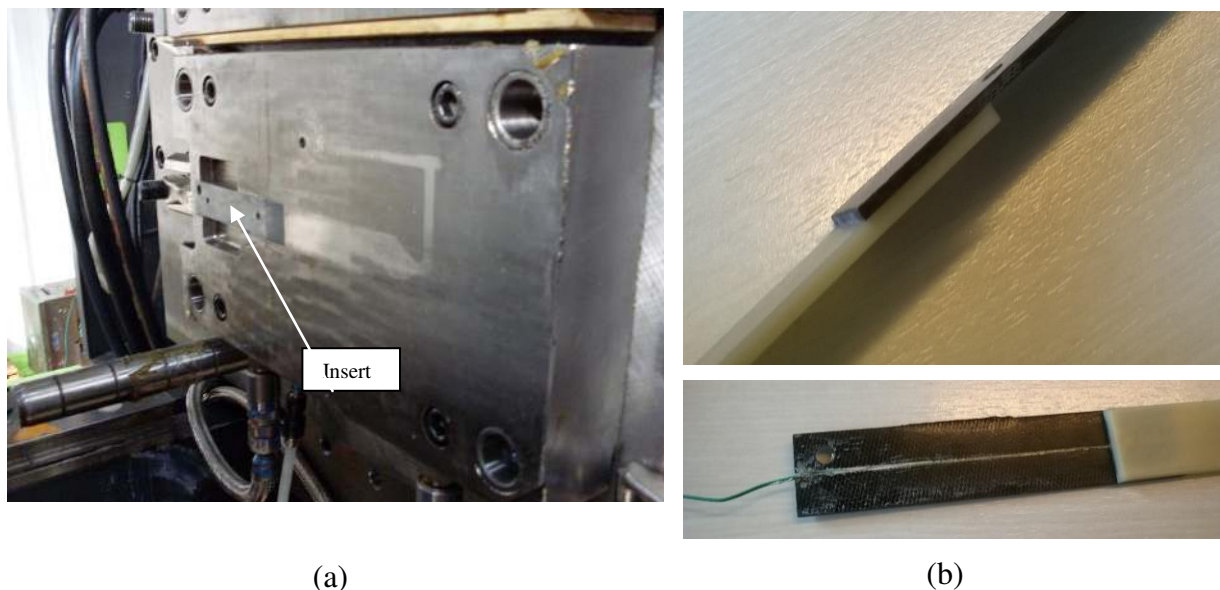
Empreinte de la cavité moulante (a) insert surmoulé (b)
